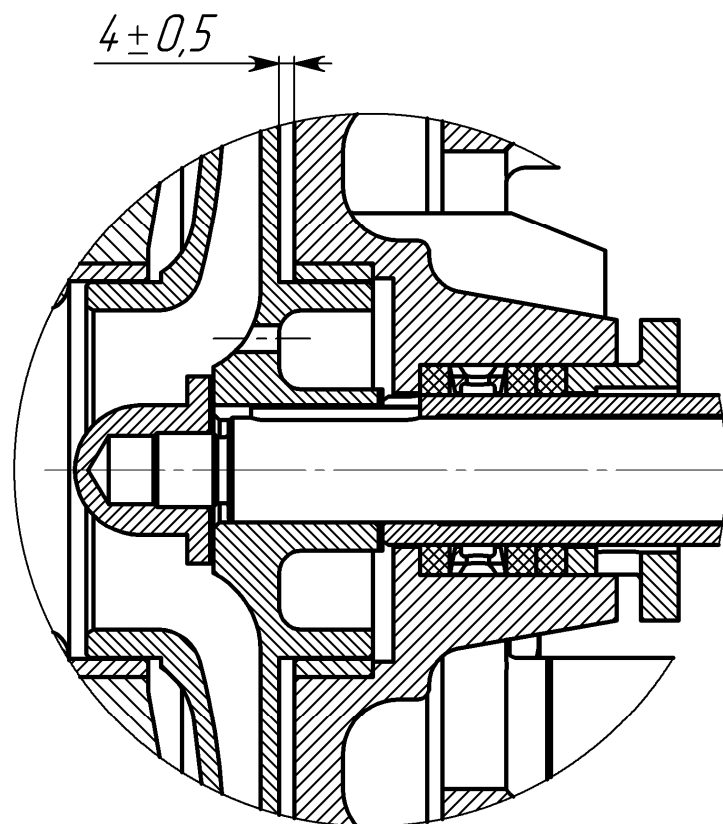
Установочный размер колеса рабочего для насоса X-80-50-200
